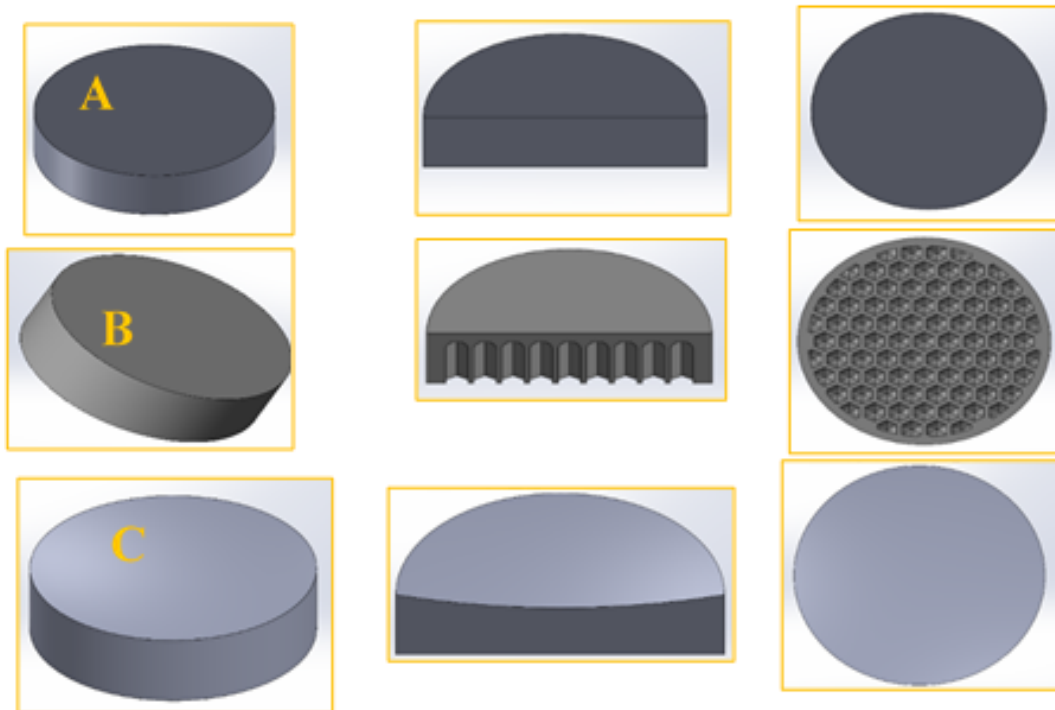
Diseño CAD de las piezas. (A) pieza plana con estructura interna sólida, (B) pieza plana con estructura en forma de panal y (C) cóncavo R100.
